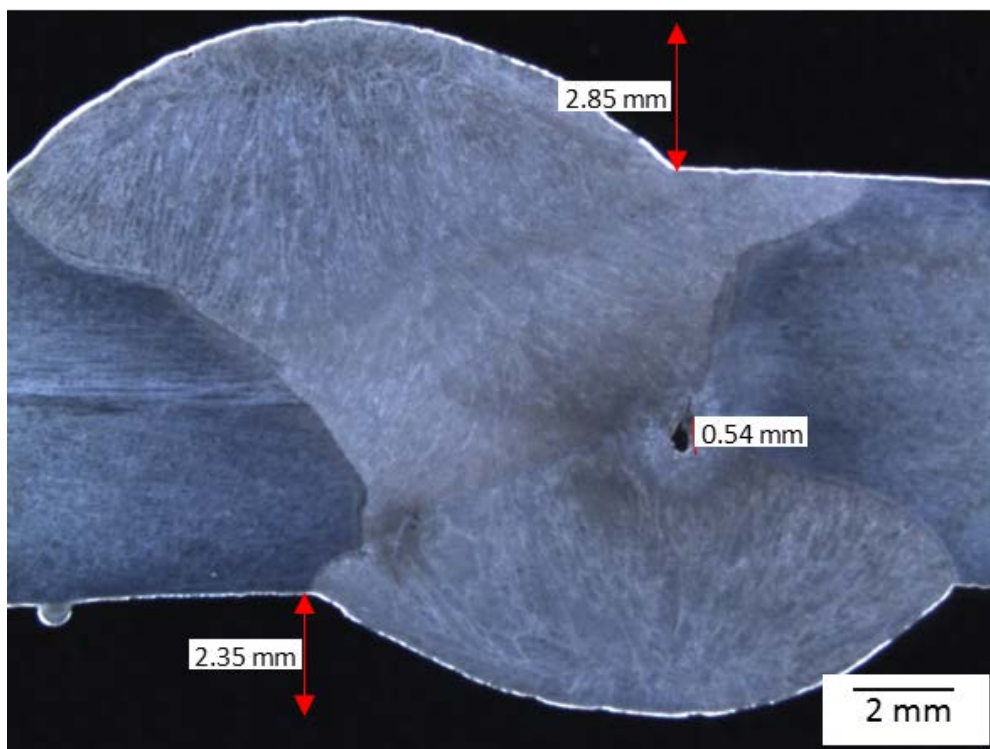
Imagen por macrografía óptica de la soldadura con las dimensiones de las propiedades de la soldadura.
